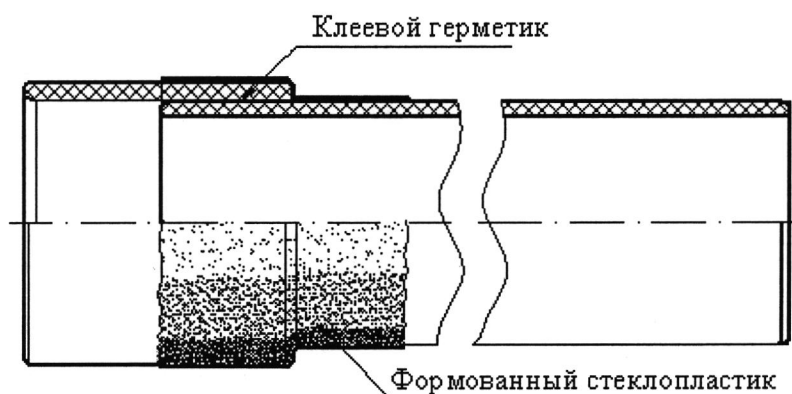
Поставка труб с закрепленным раструбом из заготовки муфты без уплотнителей
